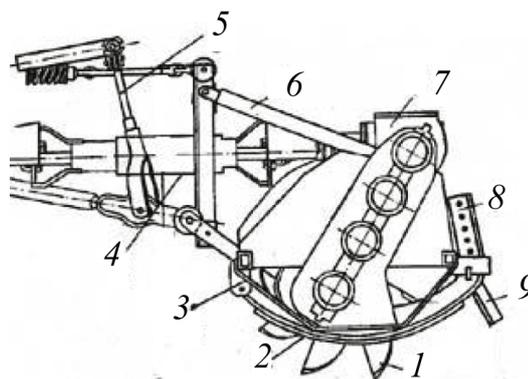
Фреза ФЛУ-0,8: 1 – ведомый диск с ножами; 2 – опорная лыжа; 3 – рама; 4 – карданный привод; 5 – навесная система трактора; 6 – навеска фрезы; 7 – редуктор; 8 – регулировочный кронштейн; 9 – гребенка
